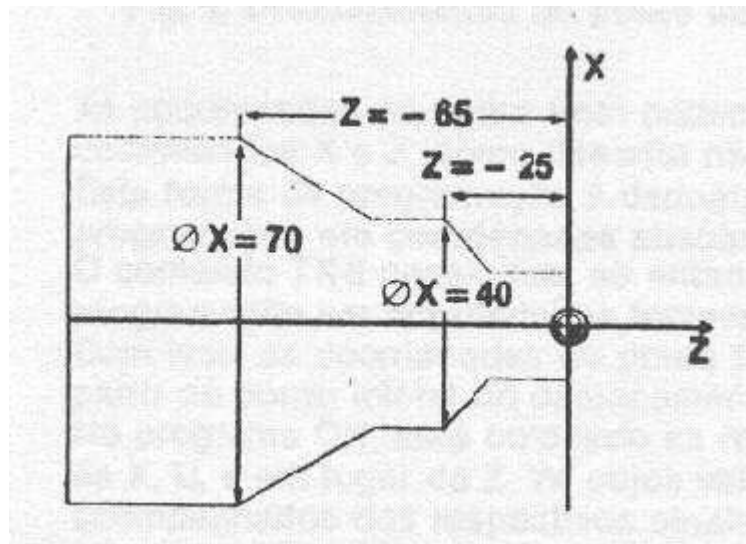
Sistema de Coordenadas (adaptado de IFAO,1984)
